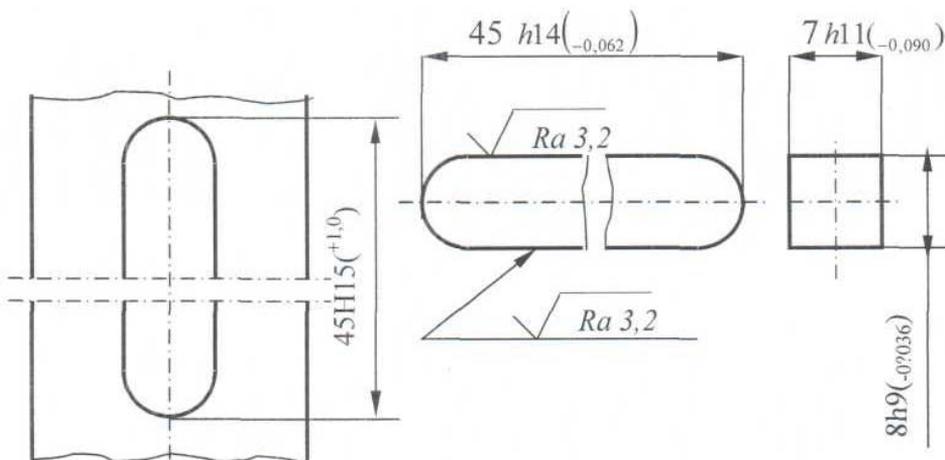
Обозначение допусков размеров деталей шпоночного соединения
